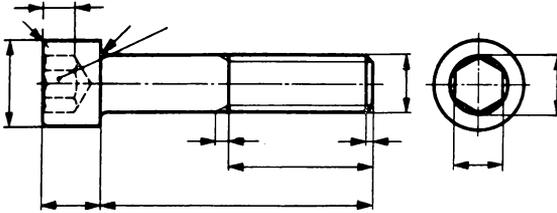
Bemaßte Zylinderschraube mit Innensechskant
